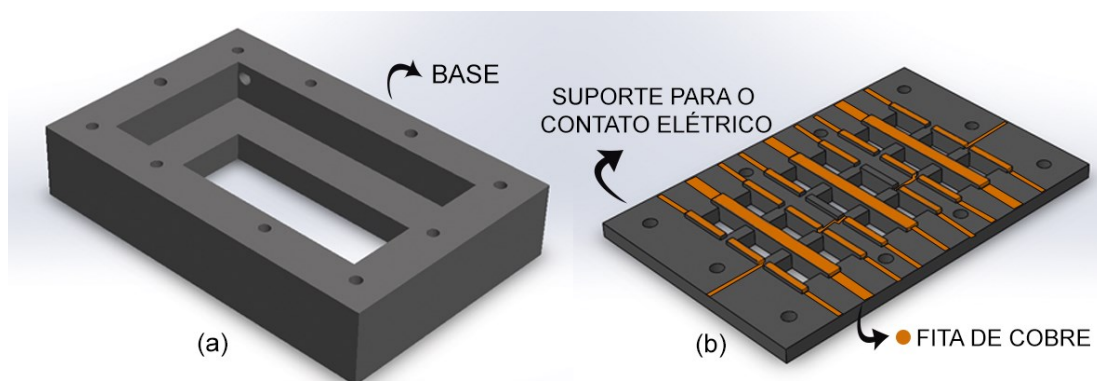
a) Desenho para impressão 3D da base do porta-amostra, com espaço central reservado para a placa-aquecedora; b) Desenho para impressão 3D da parte superior do porta-amostra com as trilhas feitas a partir de fita de cobre para a realização do contato elétrico com os sensores. Fonte: próprio autor.
